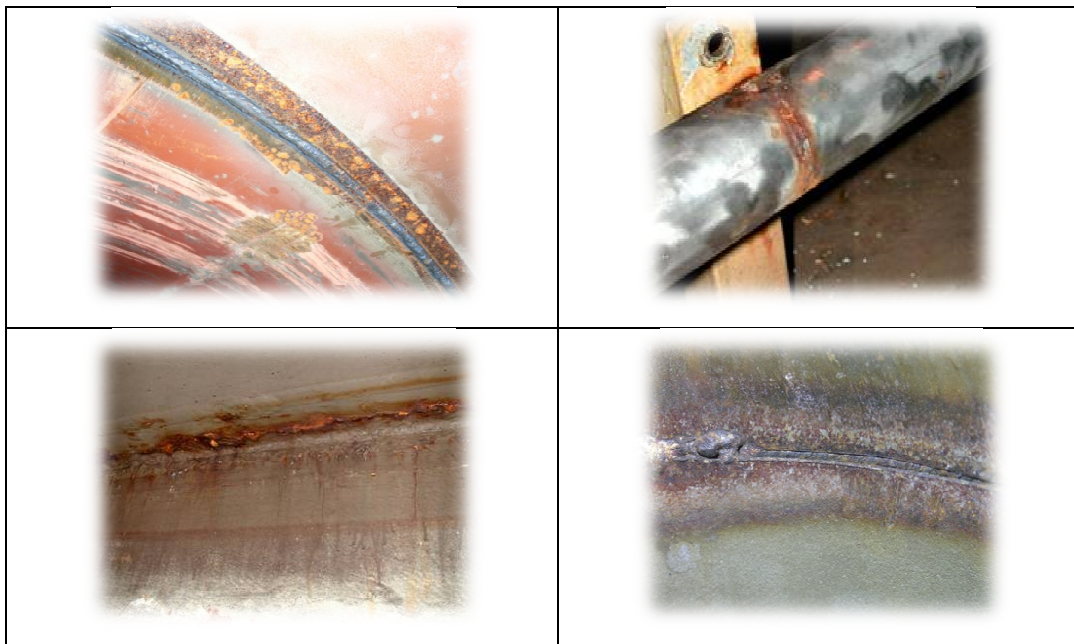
Exemplos de corrosão em soldadura [31,32,33].
